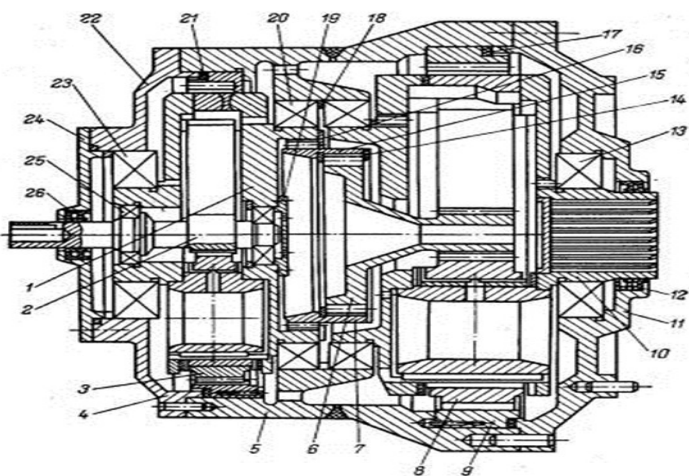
Планетарний редуктор центрифуги ОГШ-353К-02:
